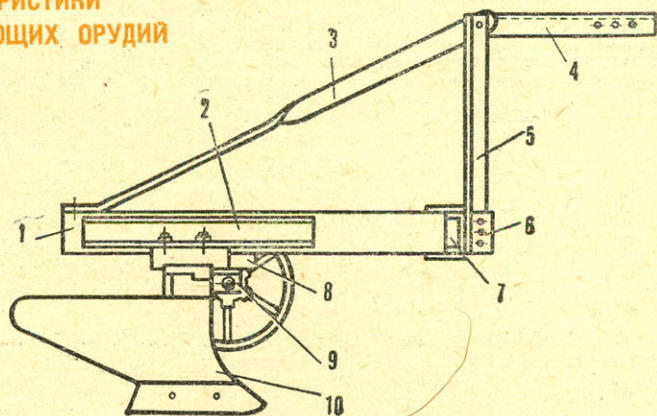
Плуг конструкции юных воиловцев школы № 51: 1 — основной брус рамы; 2 — брус крепления корпуса; 3 — стойка навески; 4 — растяжка; 5 — стойка; 6 — кронштейн; 7 — брус прицепа; 8 — сменный брусон; 9 — угольник; 10 — лемех; 11 — ось; 12 — растяжка; 13 — кронштейн.
